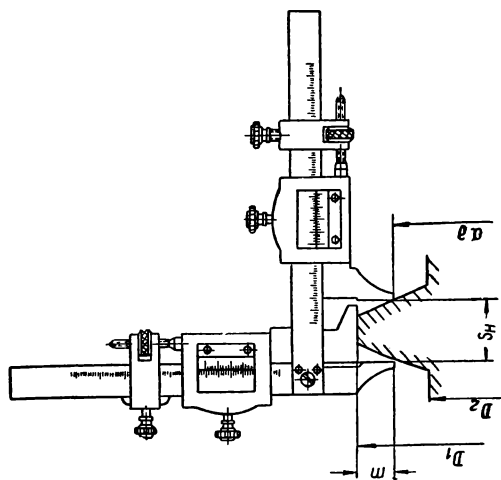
Измерение профиля зуба червяка с помощью зубомера.
